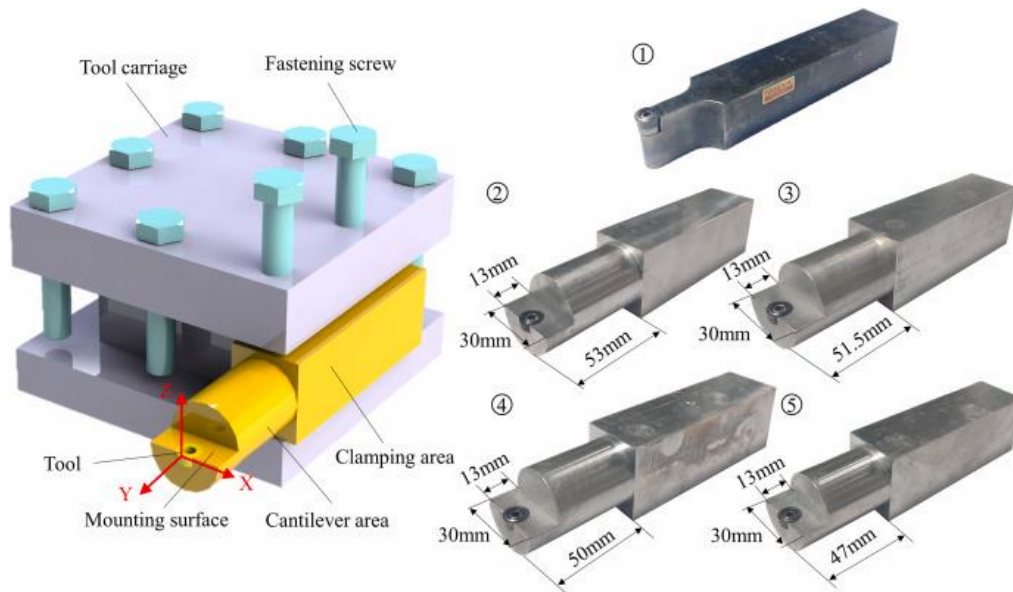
Звичайний і самозбудливі вібраційні тримачі токарного різця [2]
